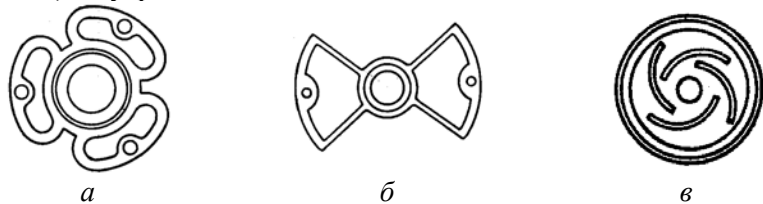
Конструкции паучковых центрирующих шайб: *a* и *б* – внешние; *в* – внутренняя.
